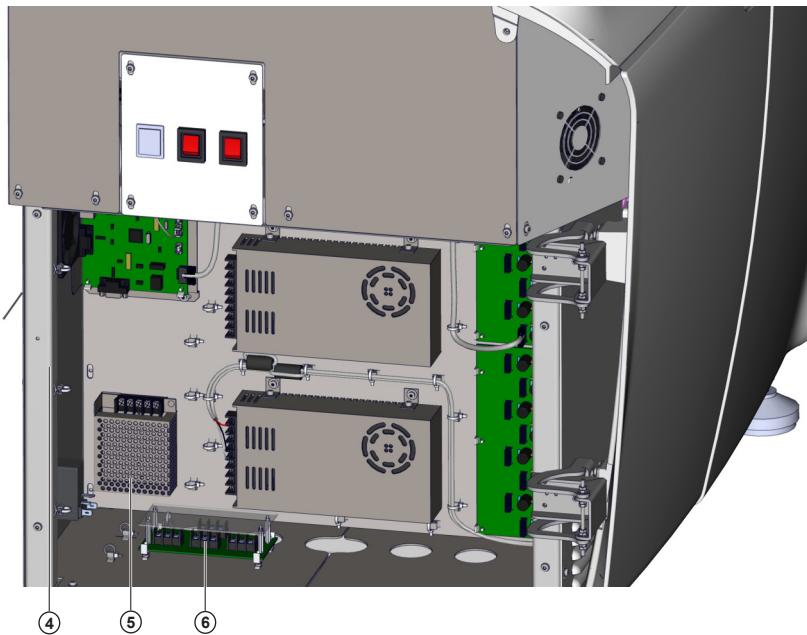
Montaje fuente alimentación módulo ISE
